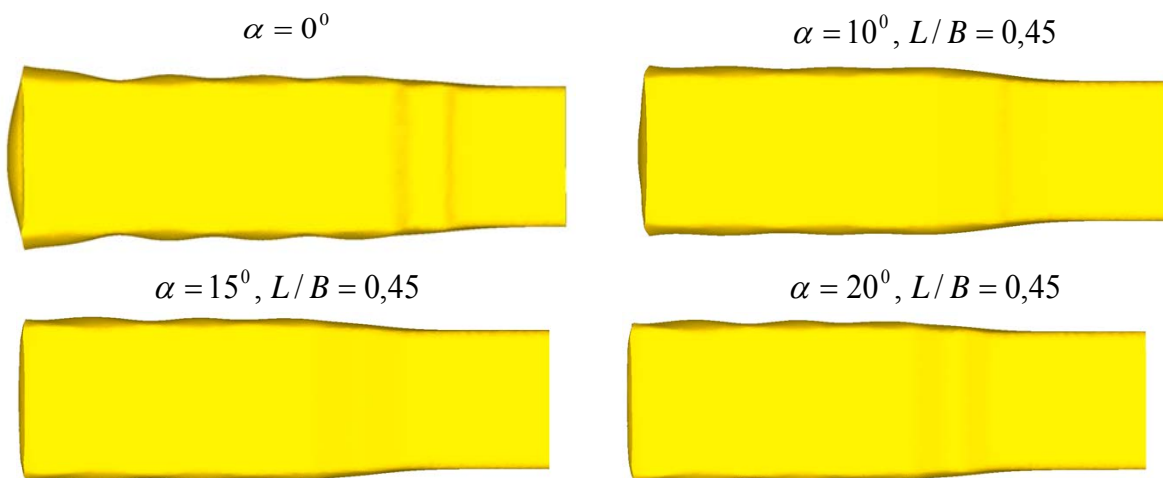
Зовнішній вигляд заготовки після протяжки бойками різних розмірів (вид зверху) при сумарному відносному стисненні заготовки, рівному 0,3 (два проходи) і подачі, рівній 2/3 ширини бойка
